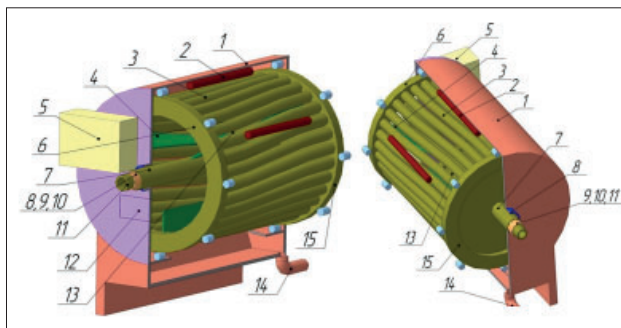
Резонаторная камера: 1 – цилиндрический экранирующий корпус; 2 – лампы-гриль; 3 – трубчатая резонаторная камера; 4 – лопасти; 5 – генераторный блок; 6 – кольцевая труба; 7 – полый вал; 8 – подшипниковый узел; 9 – диэлектрическая прокладка; 10 – стопорная гайка; 11 – муфта; 12 – люк; 13 – щель между трубами; 14 – сливной патрубкок; 15 – задняя стенка резонаторной камеры
